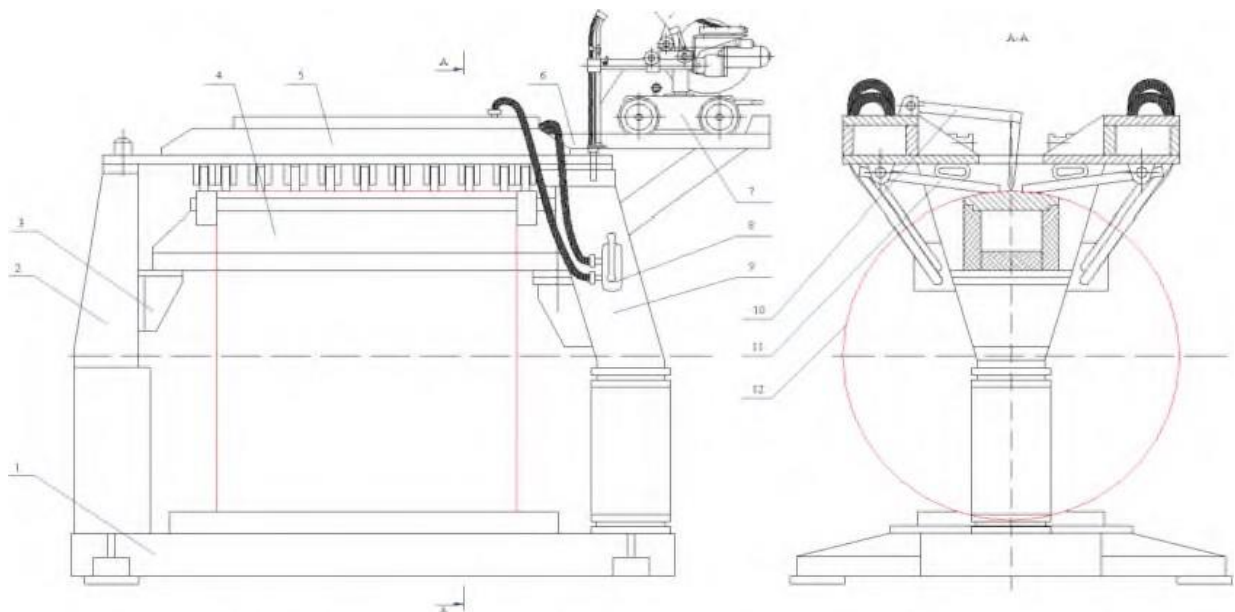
Установка для зварювання поздовжнього шва обичайки зварного виробу
